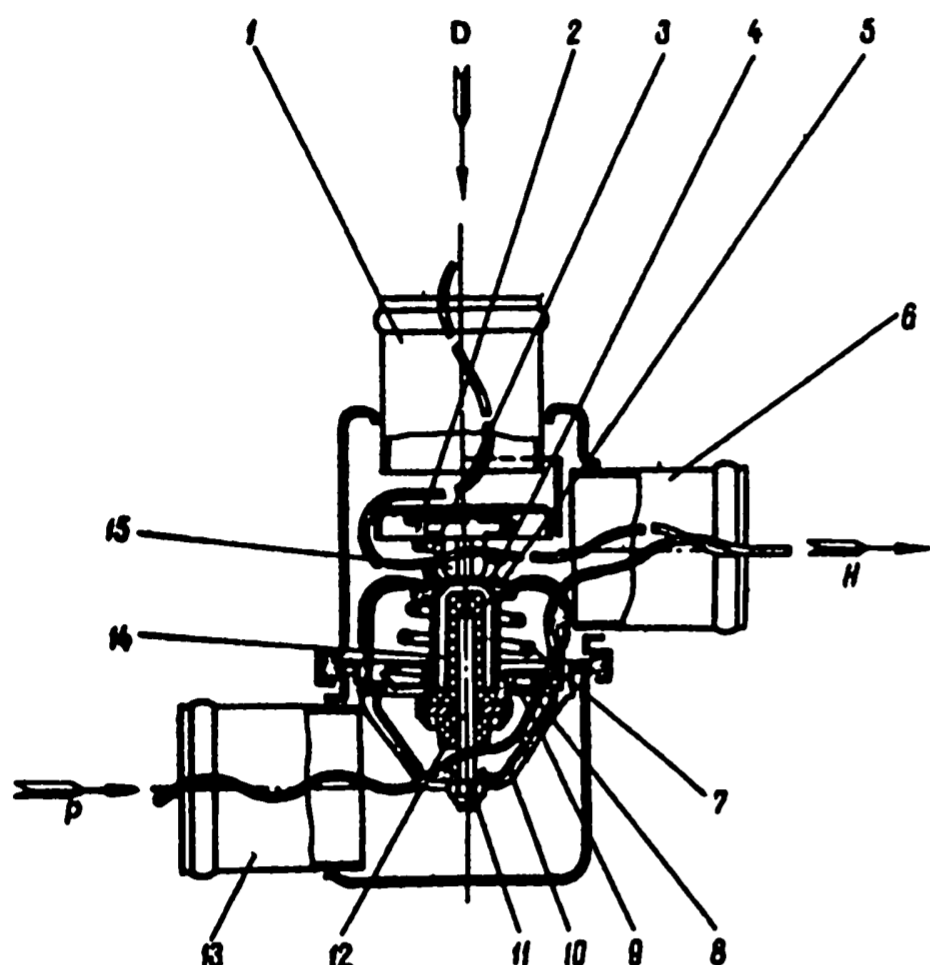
Термостат: 1 - входной патрубок (от двигателя); 2 - перепускной клапан; 3 - пружина перепускного клапана; 4 - стакан; 5 - резиновая вставка; 6 - выходной патрубок; 7 - пружина основного клапана; 8 - седло основного клапана; 9 - основной клапан; 10 - держатель; 11 - регулировочная гайка; 12 - поршень; 13 - входной патрубок от радиатора; 14 - наполнитель; 15 - обойма. D - вход жидкости от двигателя; P - вход жидкости от радиатора; H - выход жидкости к насосу
